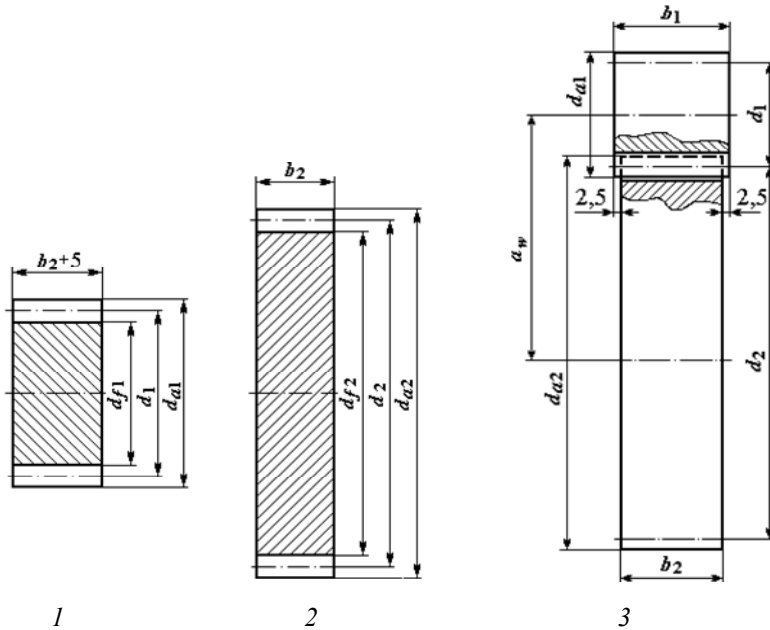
Эскизы шестерни 1, зубчатого колеса 2 и зубчатого зацепления 3
